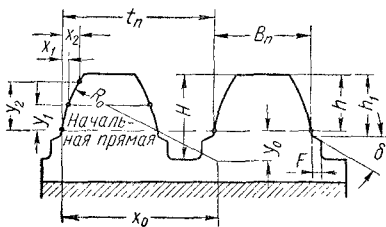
Профиль шлица и угловые параметры профиля зуба фрезы.
